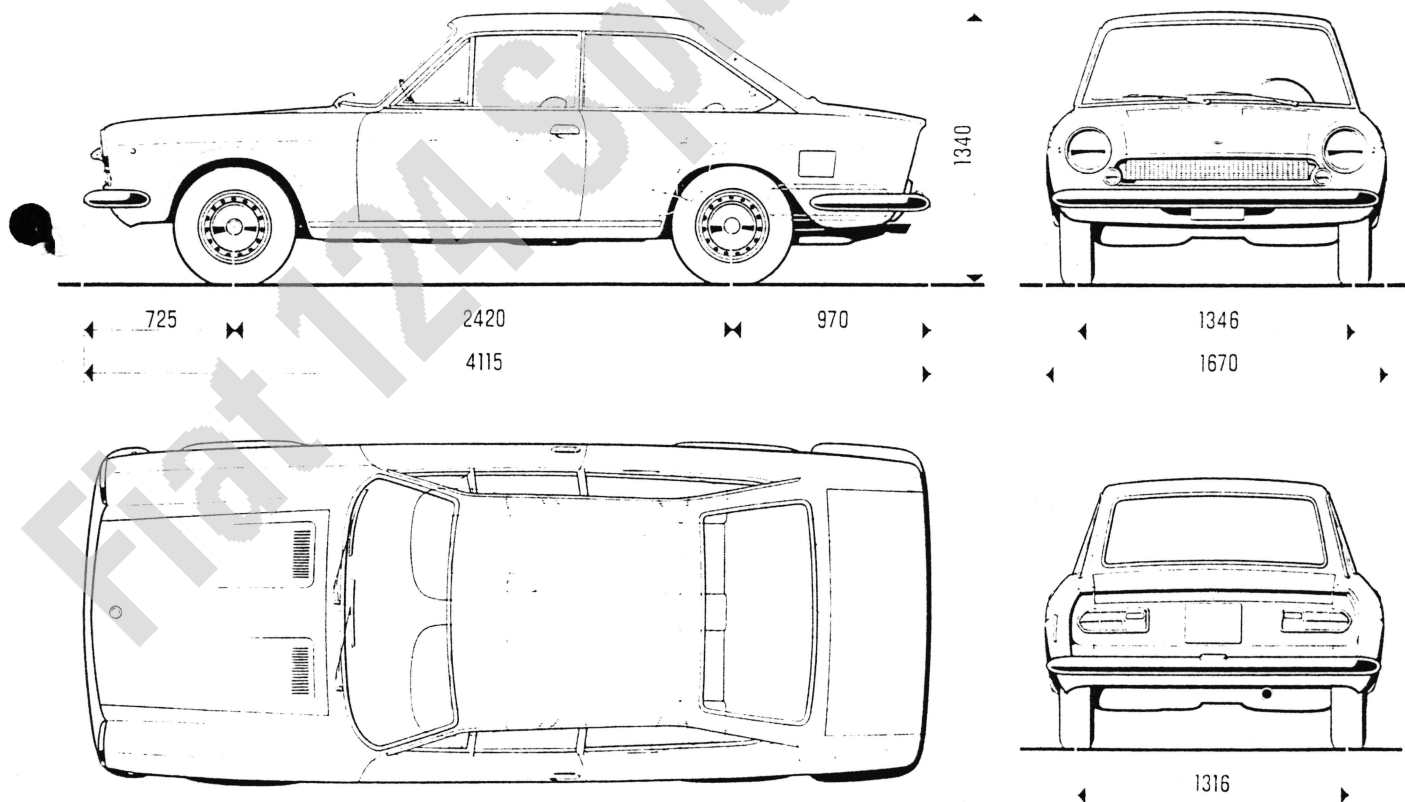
Hauptabmessungen des Fahrzeugs (die Höhe versteht sich bei unbelastetem Fahrzeug).
